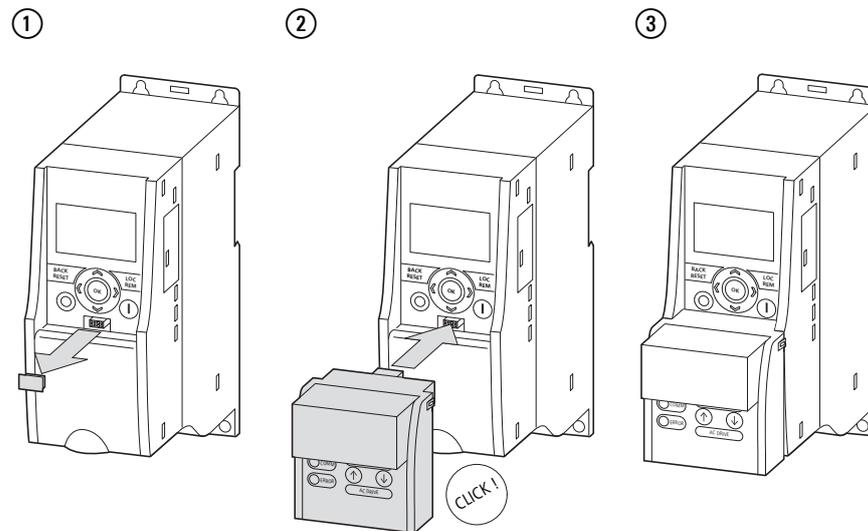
Anschaltbaugruppe MMX-COM-PC aufstecken
